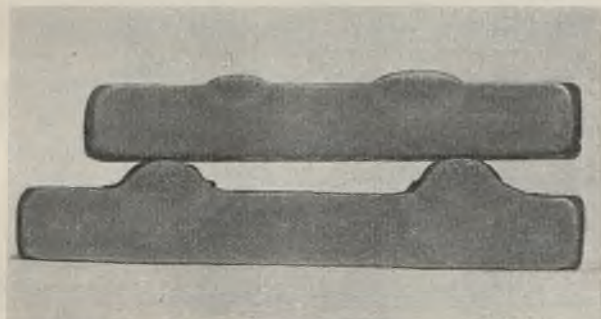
Die Wirkung des Einbrandes bei gut gezogenen Schweißraupen.
